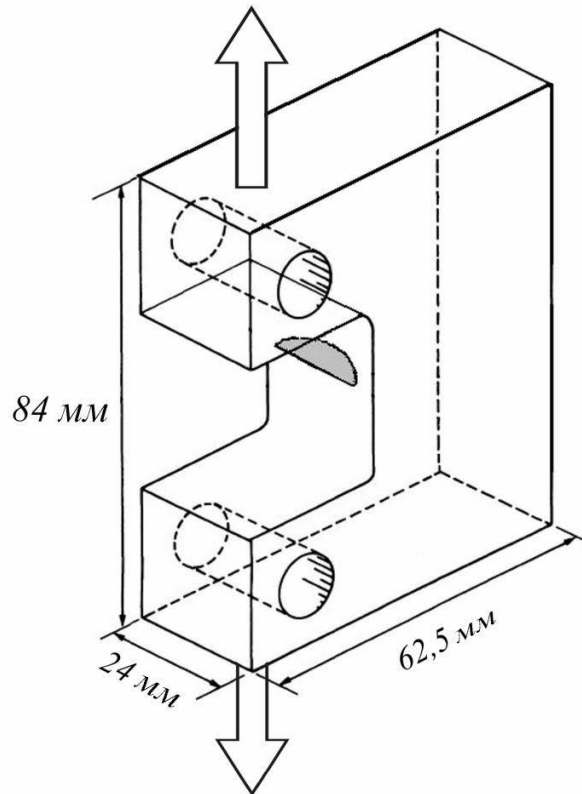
Компактный образец с полуэллиптической трещиной [76]
